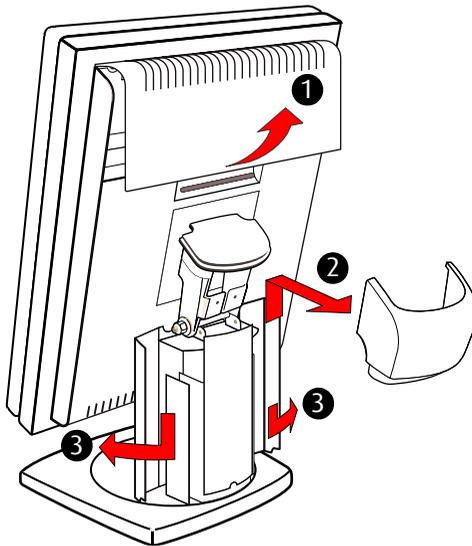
Remova as tampas antes de conectar os cabos de sinal
